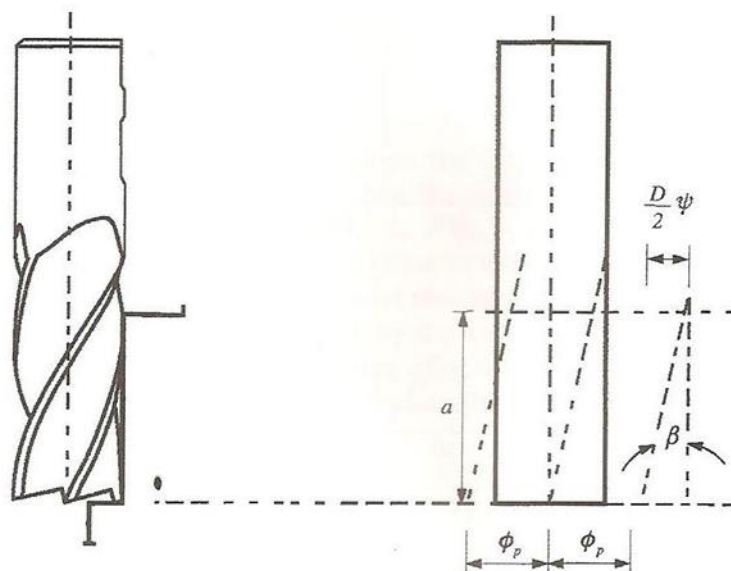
Fresa helicoidal frontal cilíndrica. [13]
